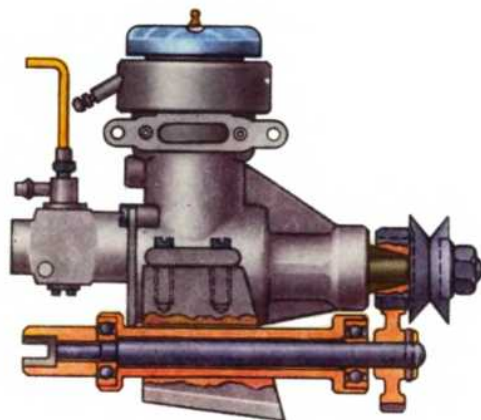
Двигатель внутреннего сгорания с редуктором.
